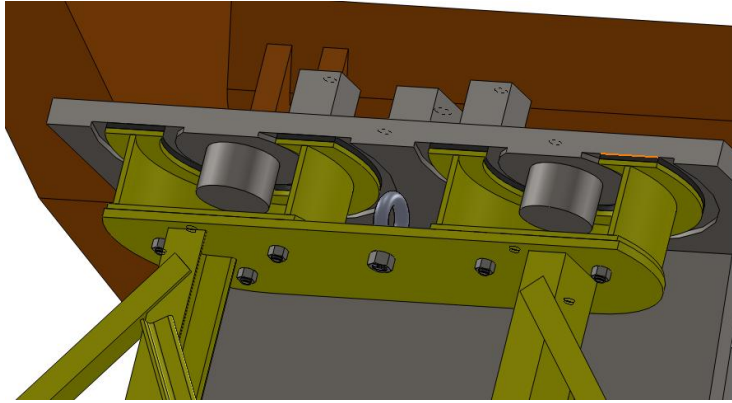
Pormenor do assentamento da Travessa Dançante nos apoios da estrutura
